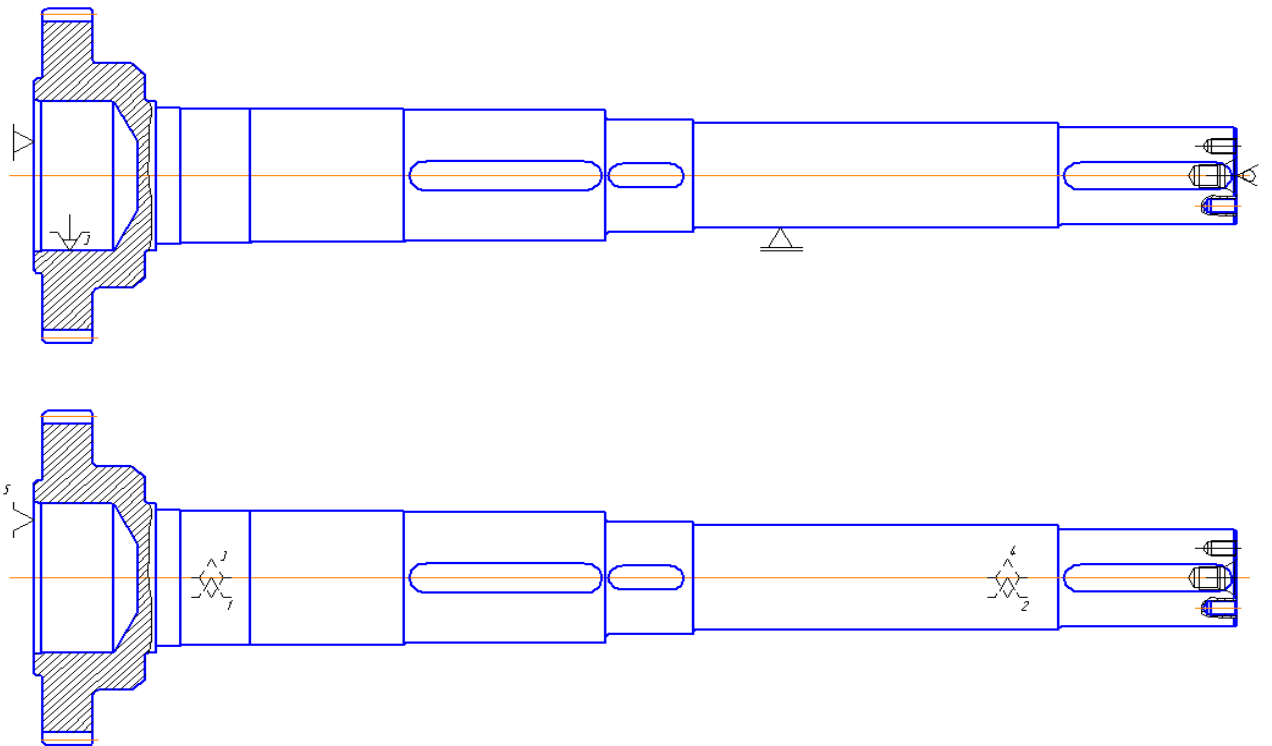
Умовна та теоретична схема базування при зубофрезерній операції
